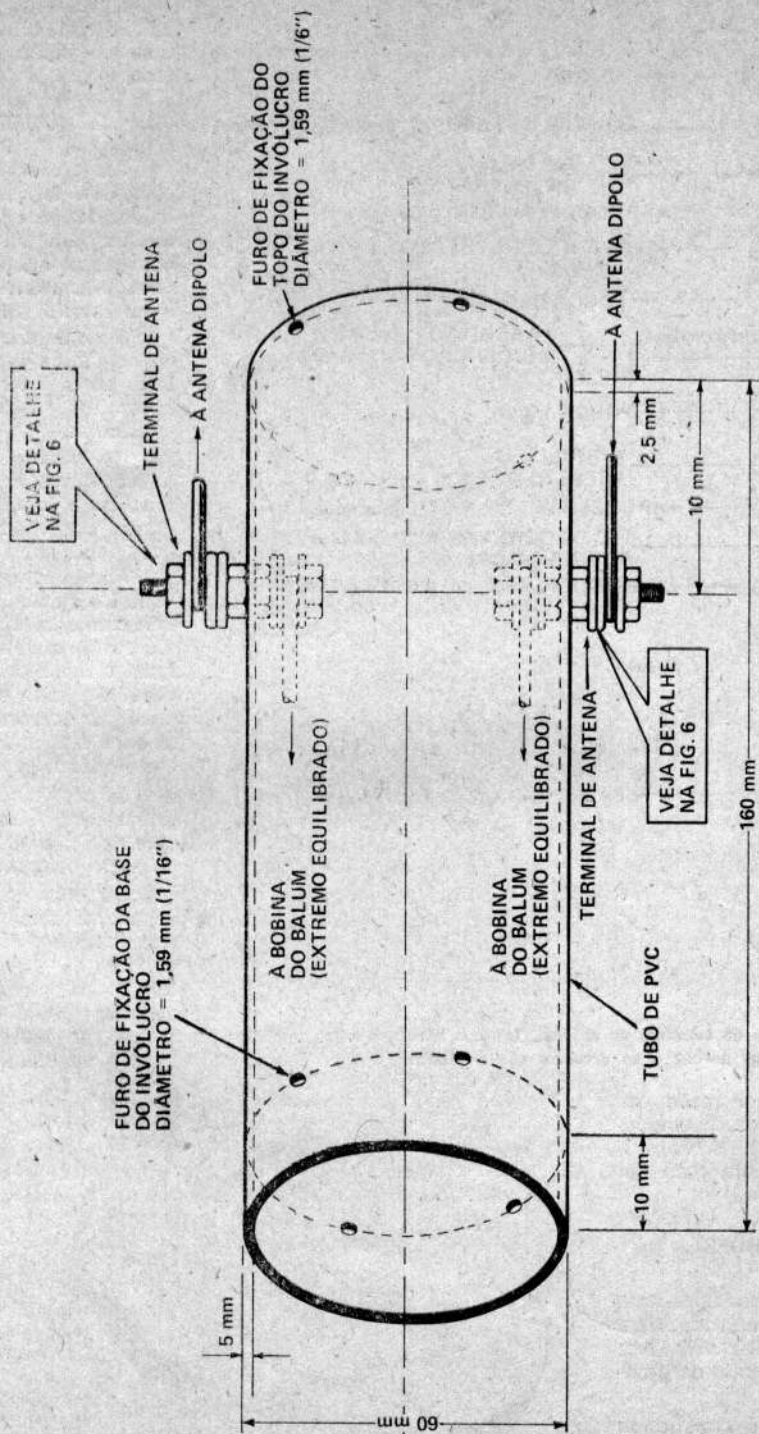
O corpo do involuço do balum, executado com tubo de PVC com 60 mm de diâmetro externo. Dimensões em milímetros.
